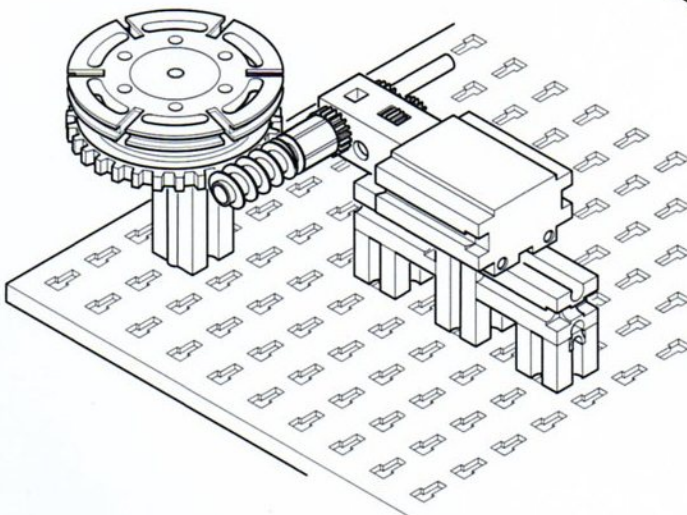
Motorgetriebe mit Schnecke und Schneckenrad
